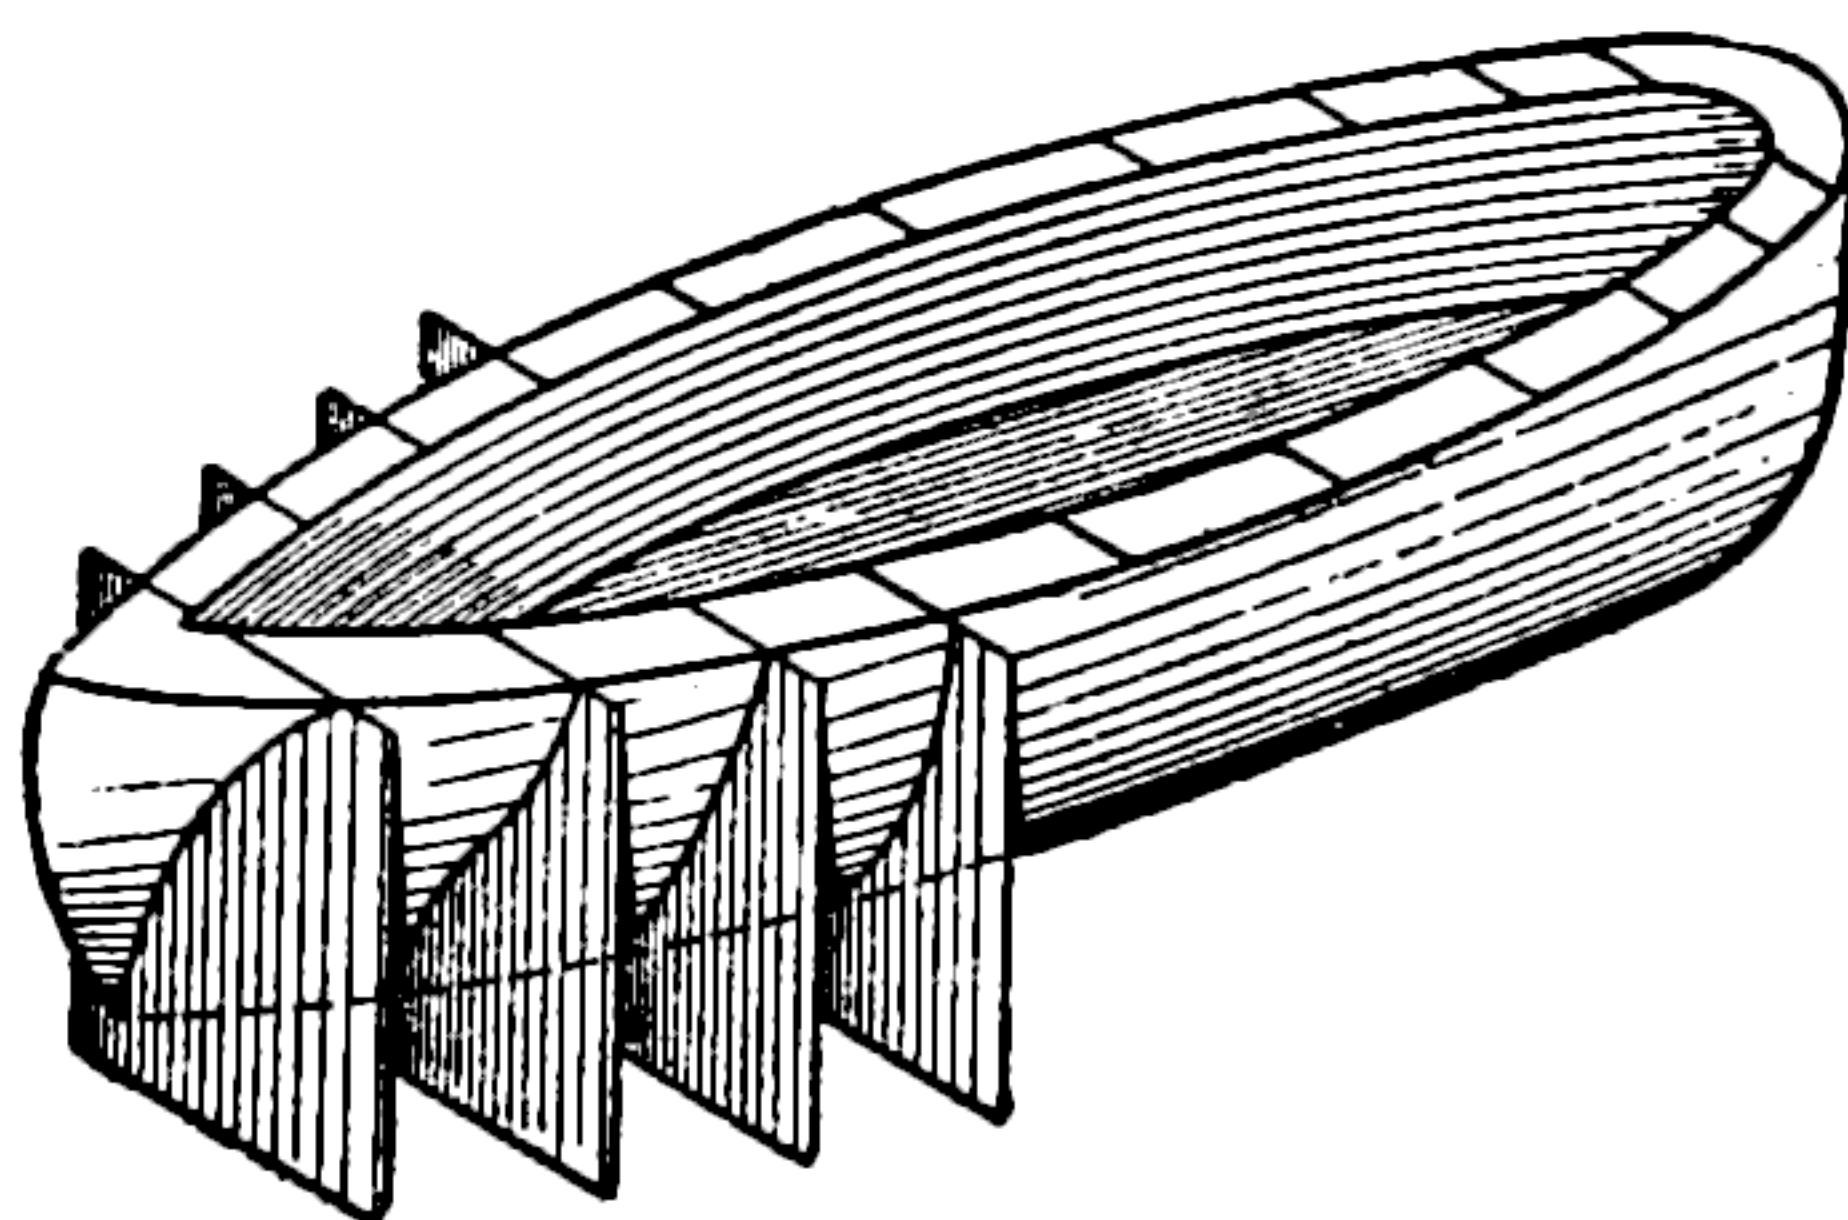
Проверка наружной обработки болванки наружными лекалами.
